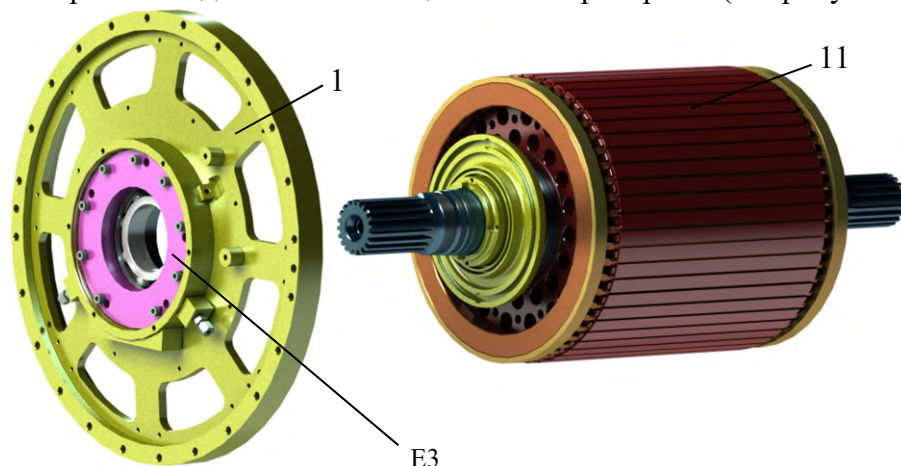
Демонтаж подшипникового щита с ротора (сторона привода)
